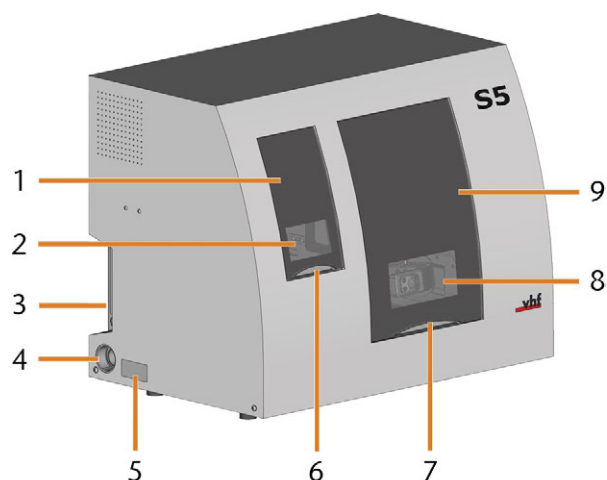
CÔTÉ AVANT DE LA MACHINE
